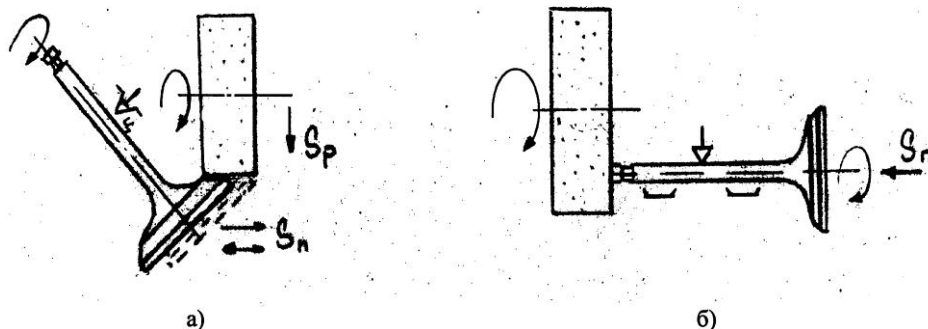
Схема шлифования фаски (а) и торца клапана (б).
